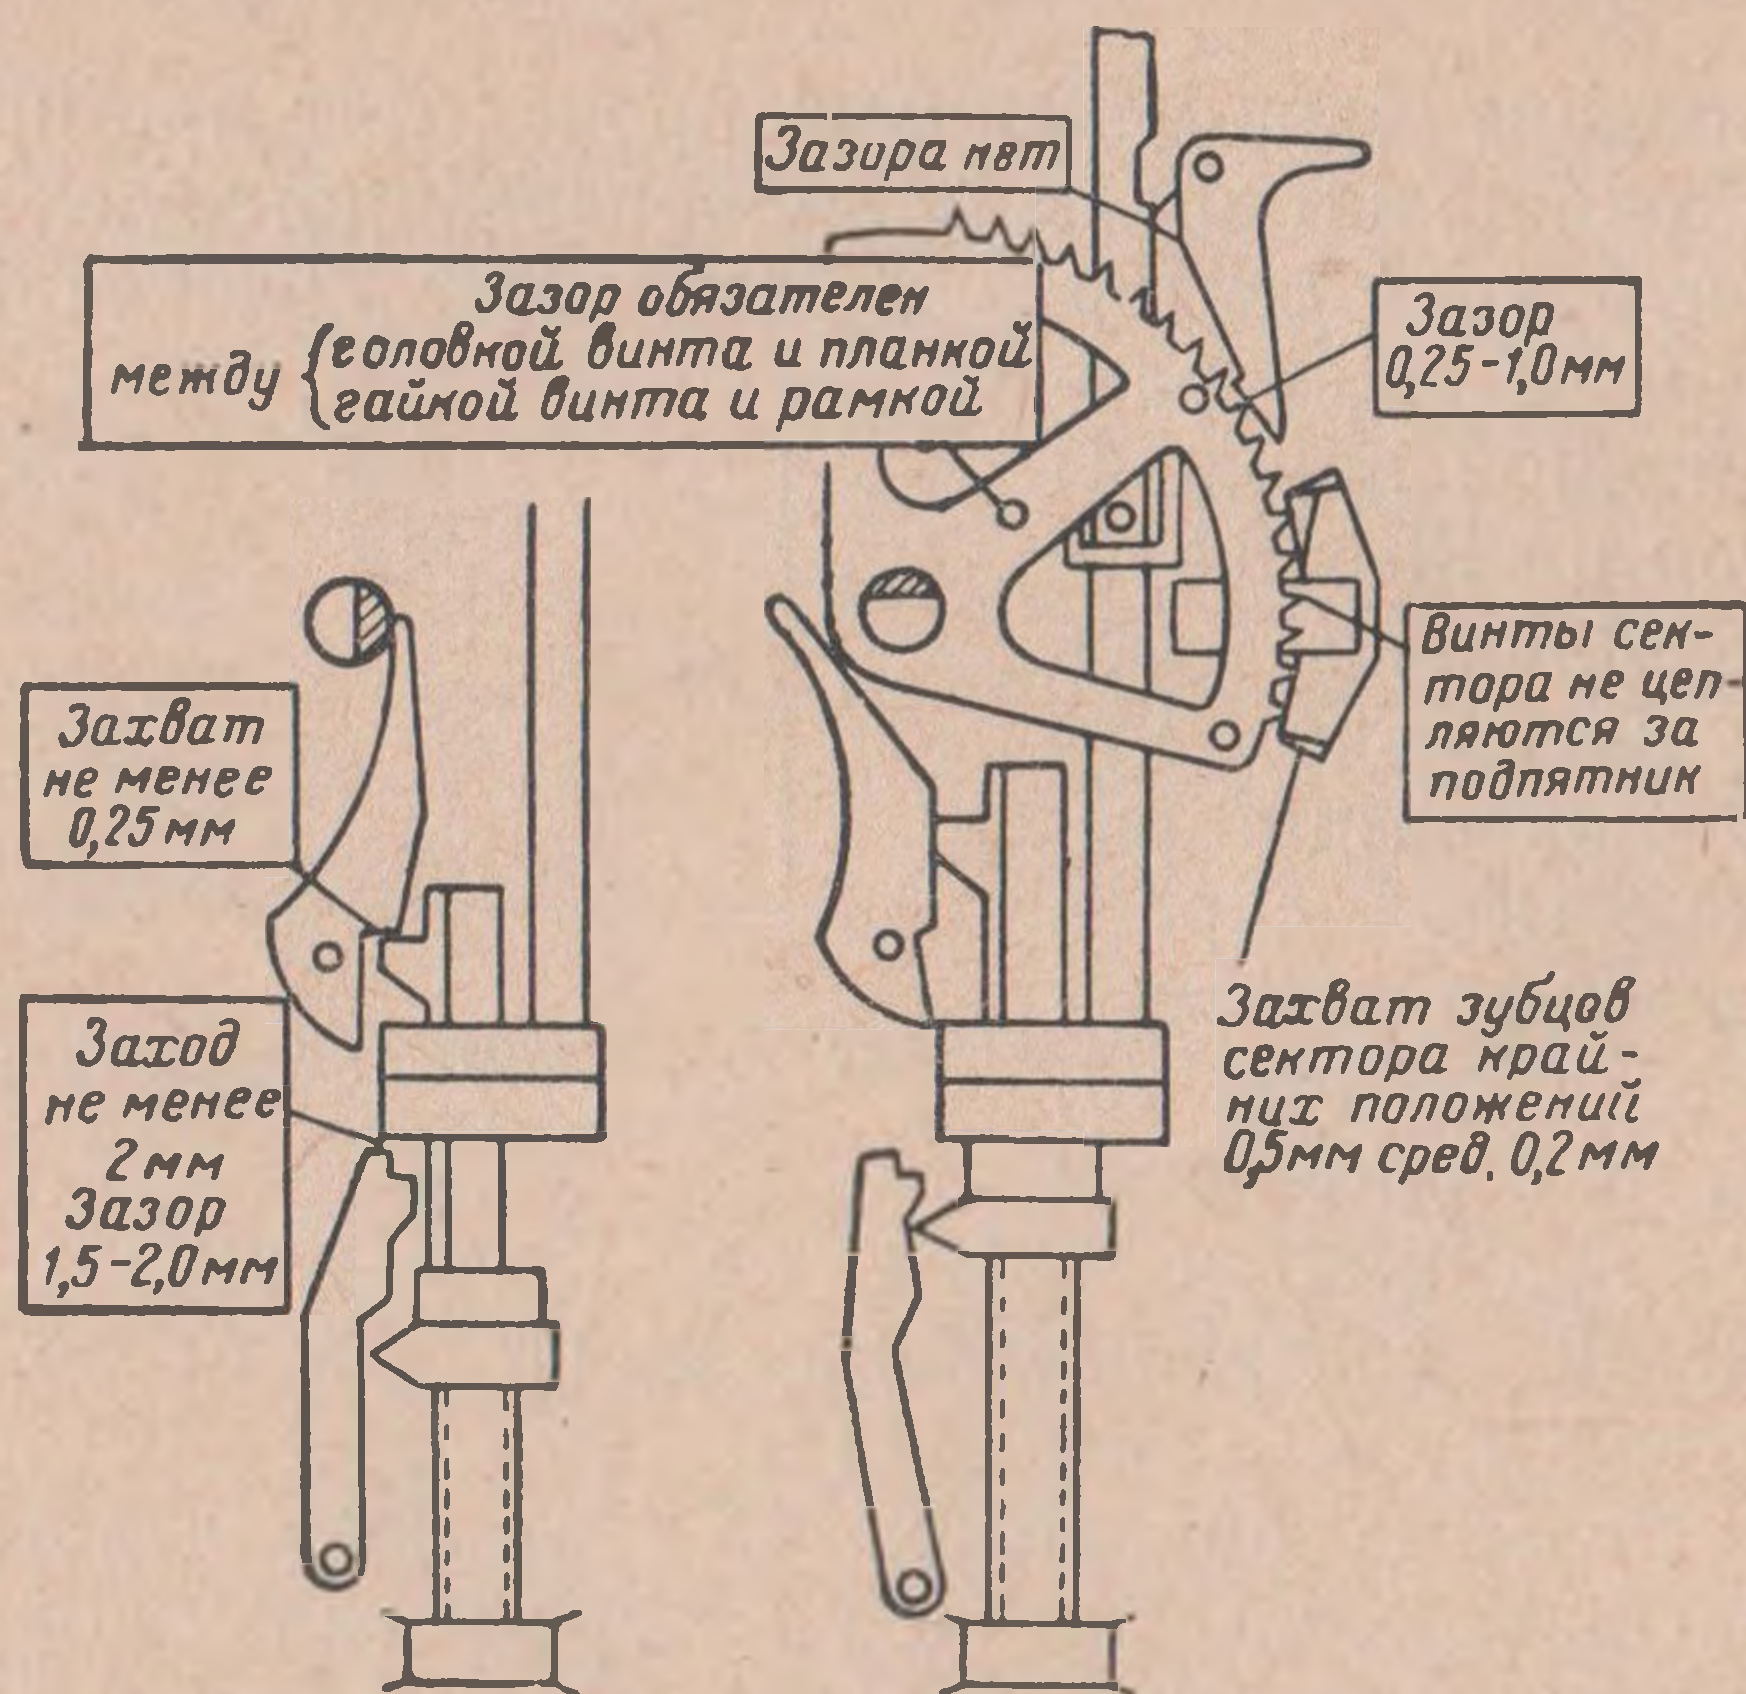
Зазоры и допуски в блок-механизме
